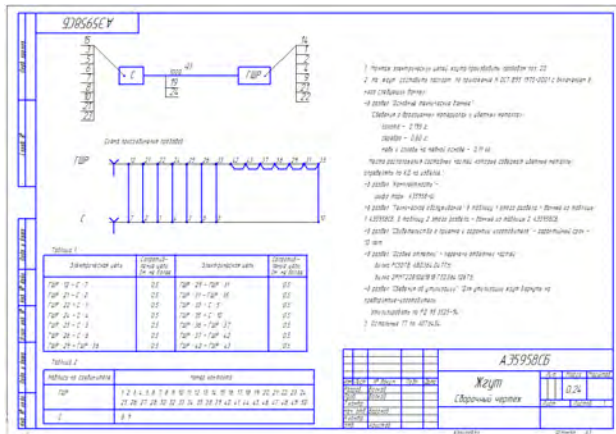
Сборочный чертёж жгута, скомпонованный в КОМПАС-3D
